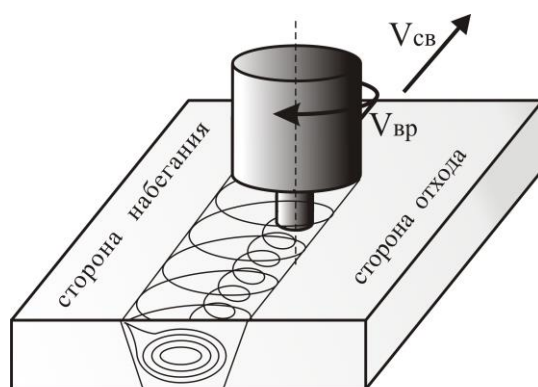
Сущность сварки трением с перемешиванием
